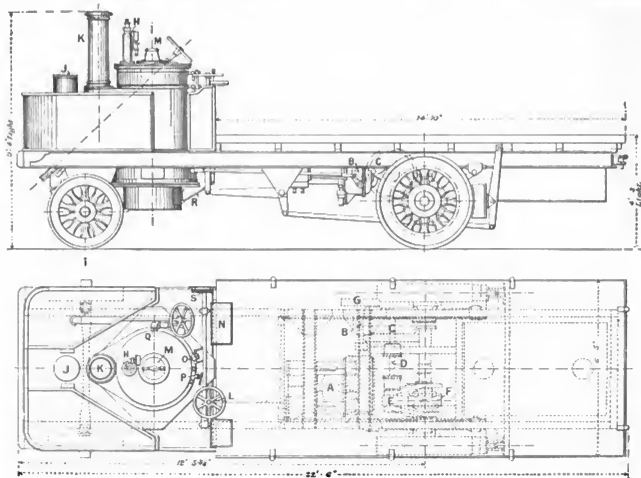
und 5. Aufriss und Grundriss des Thornycroft 7 t-Lastwagen.
